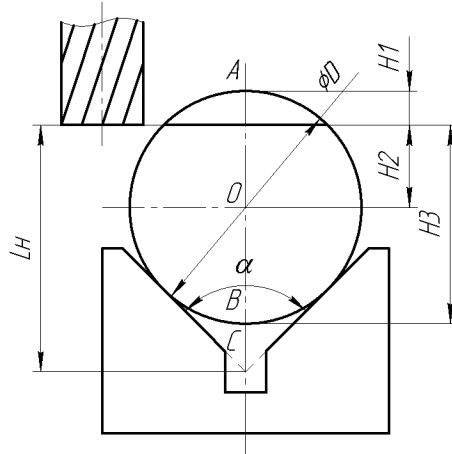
Визначення похибки базування при базуванні заготовки в призмі
